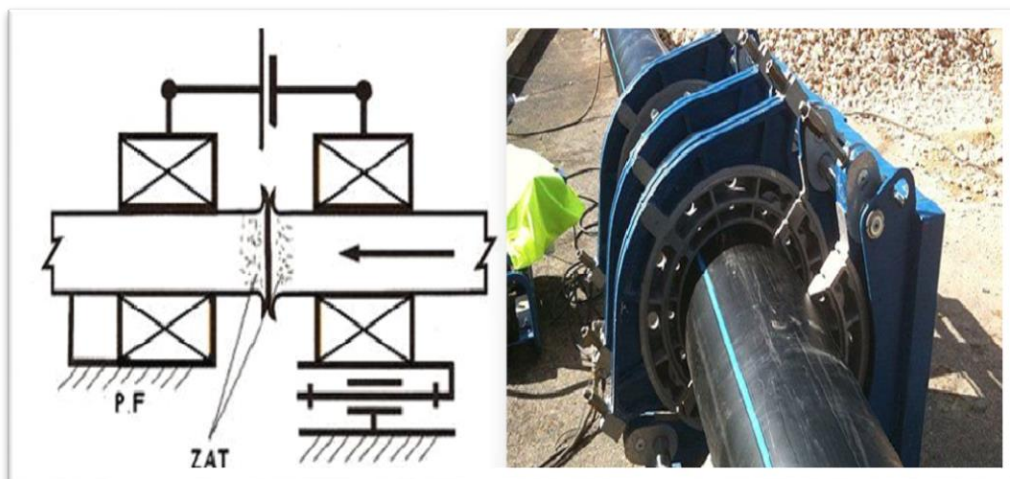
Exemple de soudage bout à bout.
